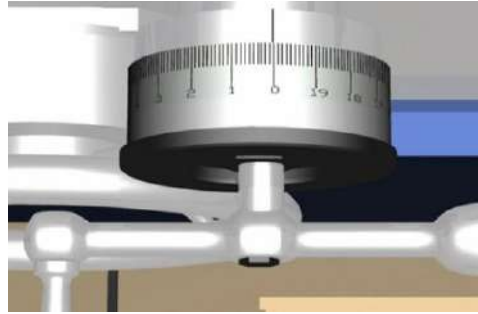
Лімба для точної установки глибини різання різцем у верстата
